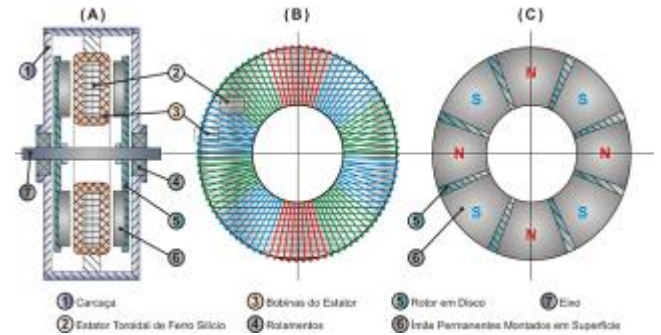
Máquina de fluxo axial do tipo toroidal ("Torus Machine"). (A) Estrutura construtiva, (B) vista frontal do estator bobinado, (C) vista frontal do disco de ímãs.
